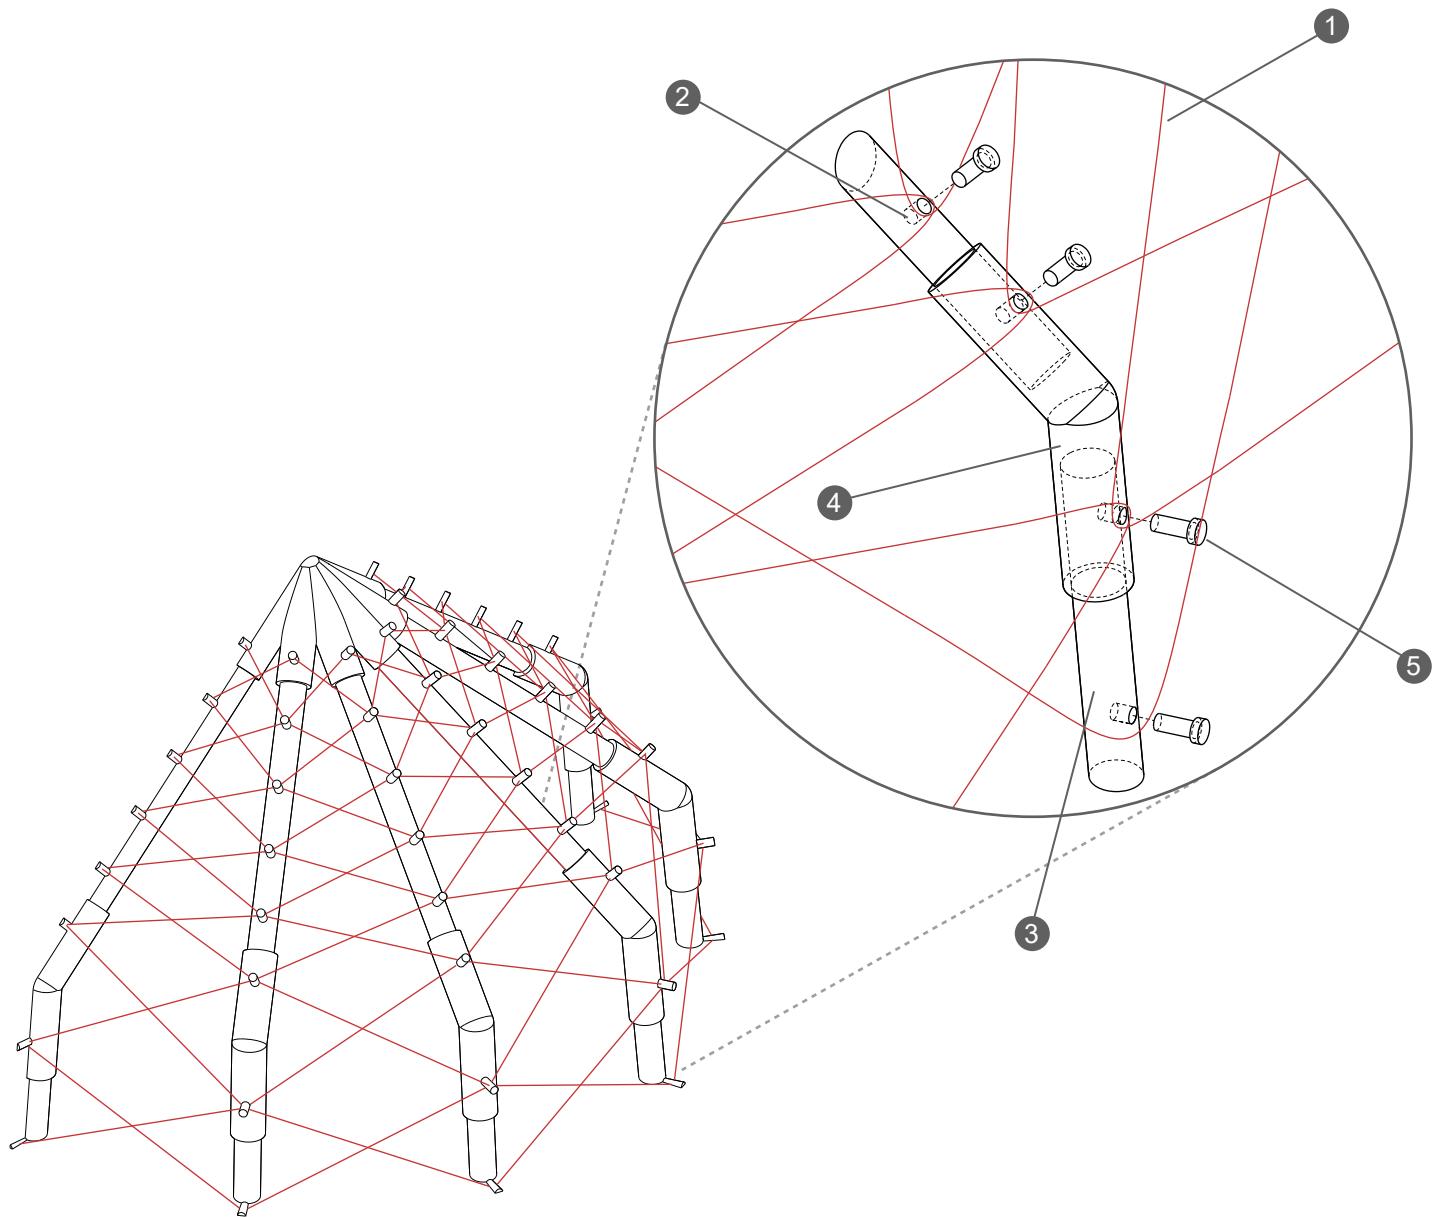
Axonométrica explotada del producto con especificaciones técnicas.
